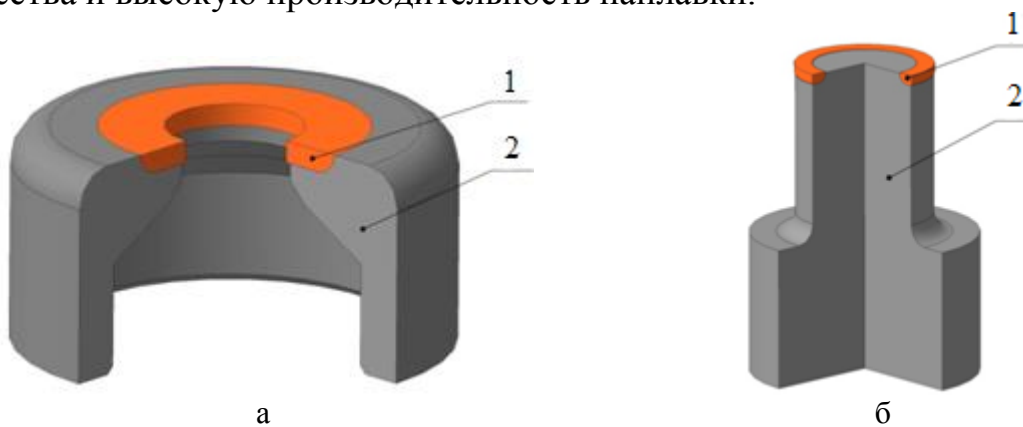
Схематичный вид рабочих элементов штампа: а – матрицы; б – пуансона; 1 – наплавленный слой быстрорежущей стали; 2 – корпус инструмента
